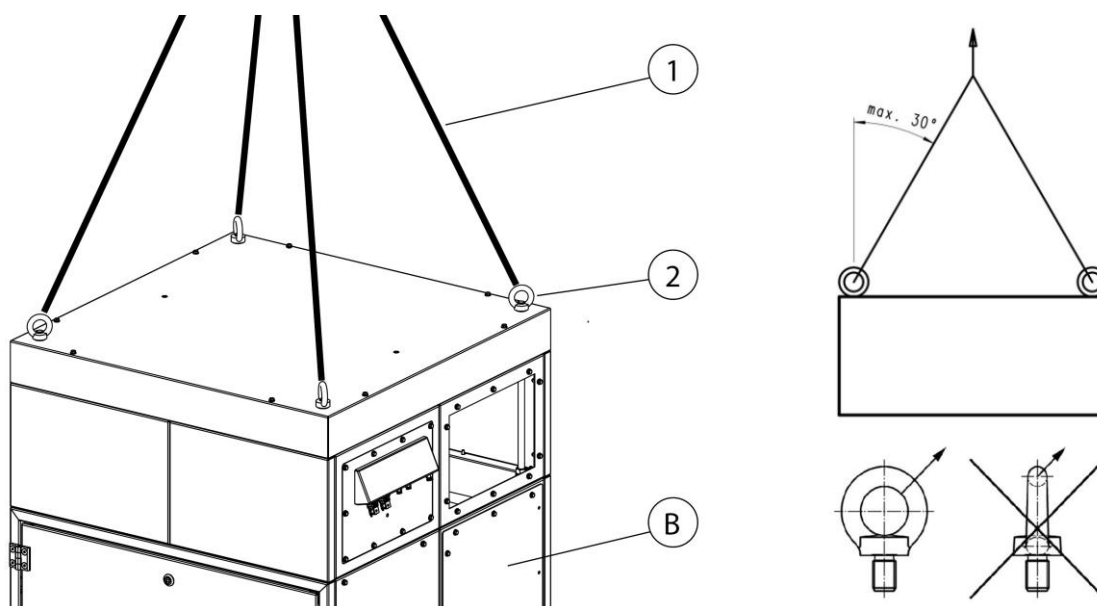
Levantamento do produto por meio de grua/equipamento de elevação
